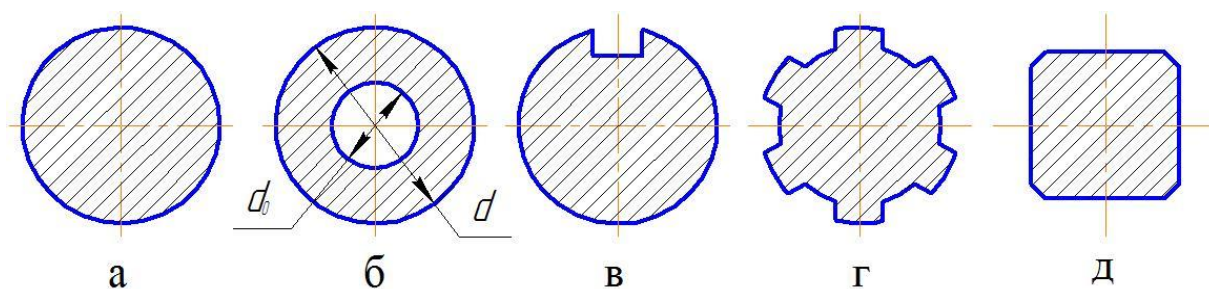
Форми поперечних перерізів валів: а – суцільний поперечний переріз; б – порожнистий всередині; в – гладкий циліндричний, із шпонковим пазом; г – шліцевий; д – прямокутний суцільний поперечний переріз
